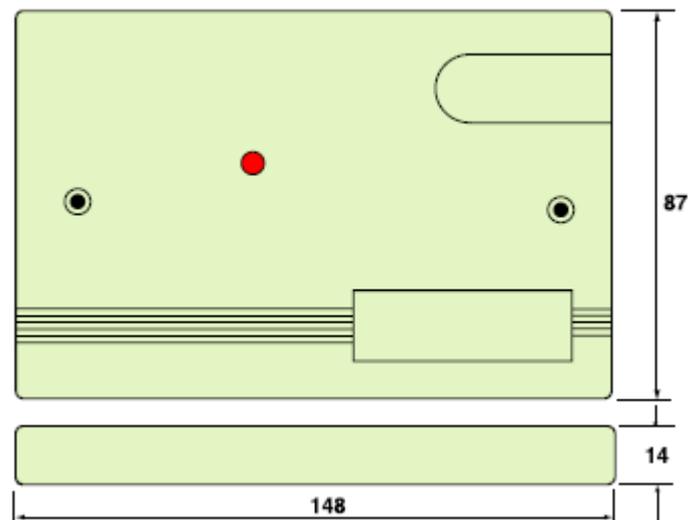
FC410LI fijado a la cubierta. Vista frontal y dimensiones
